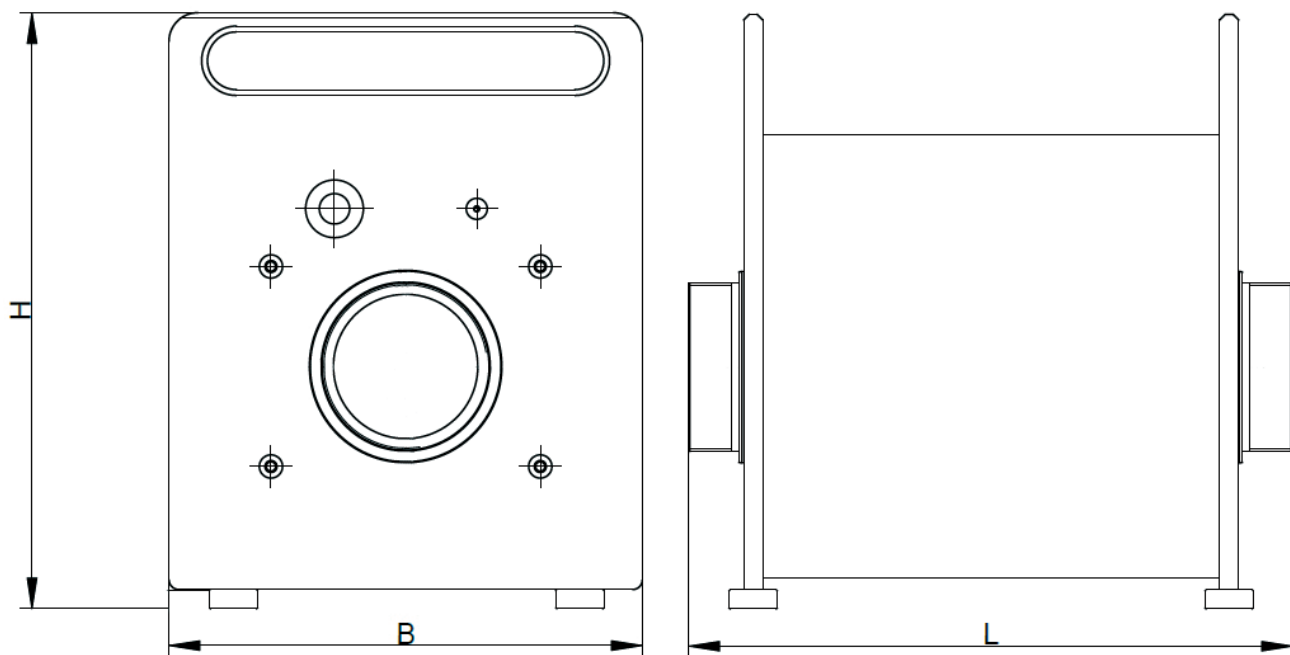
Bemaßung mag-flux® HTL Frontansicht und Seitenansicht
